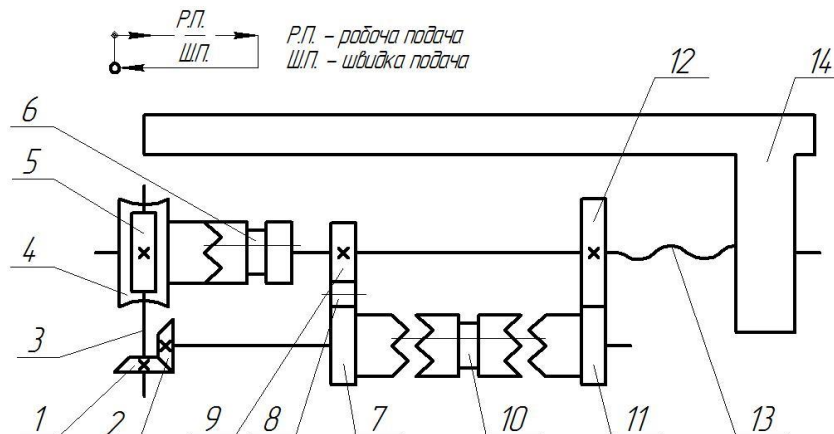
Кінематична схема механічного привода з механізмом реверсу: 1, 2 – конічна пара; 3 – ведучий вал; 4, 5 – черв’ячна передача; 6 – муфта; 7, 8, 9 – ланка реверсу; 10 – муфта; 11, 12 – циліндрична передача; 13 – ходовий гвинт; 14 – виконавчий орган
